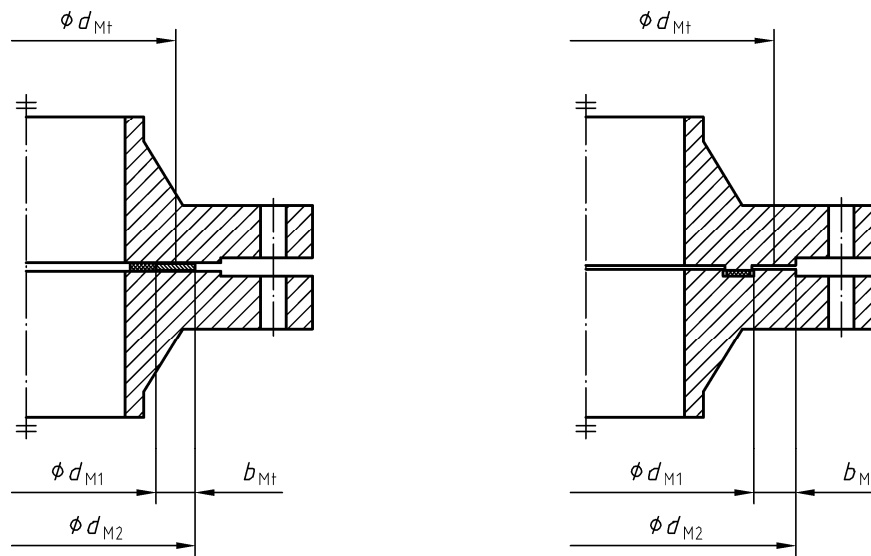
2 Ausführungen einer verschraubten Flanschverbindung mit Dichtung im Kraft-Nebenschluss: Dichtung mit Stützring und Dichtung in einer Nut, mit theoretischen Maßen
